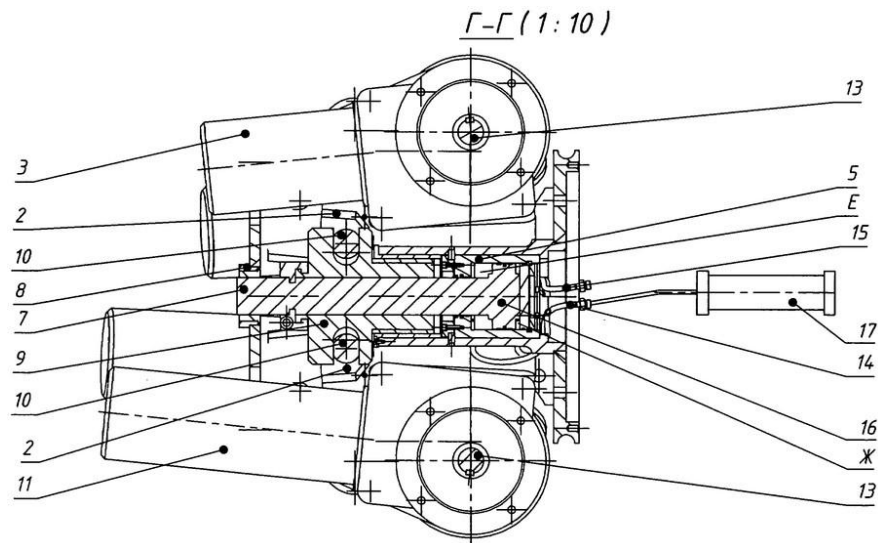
Механизм перемещения машины для сварки труб, в дальнейшем "механизм перемещения", сечение Г-Г
